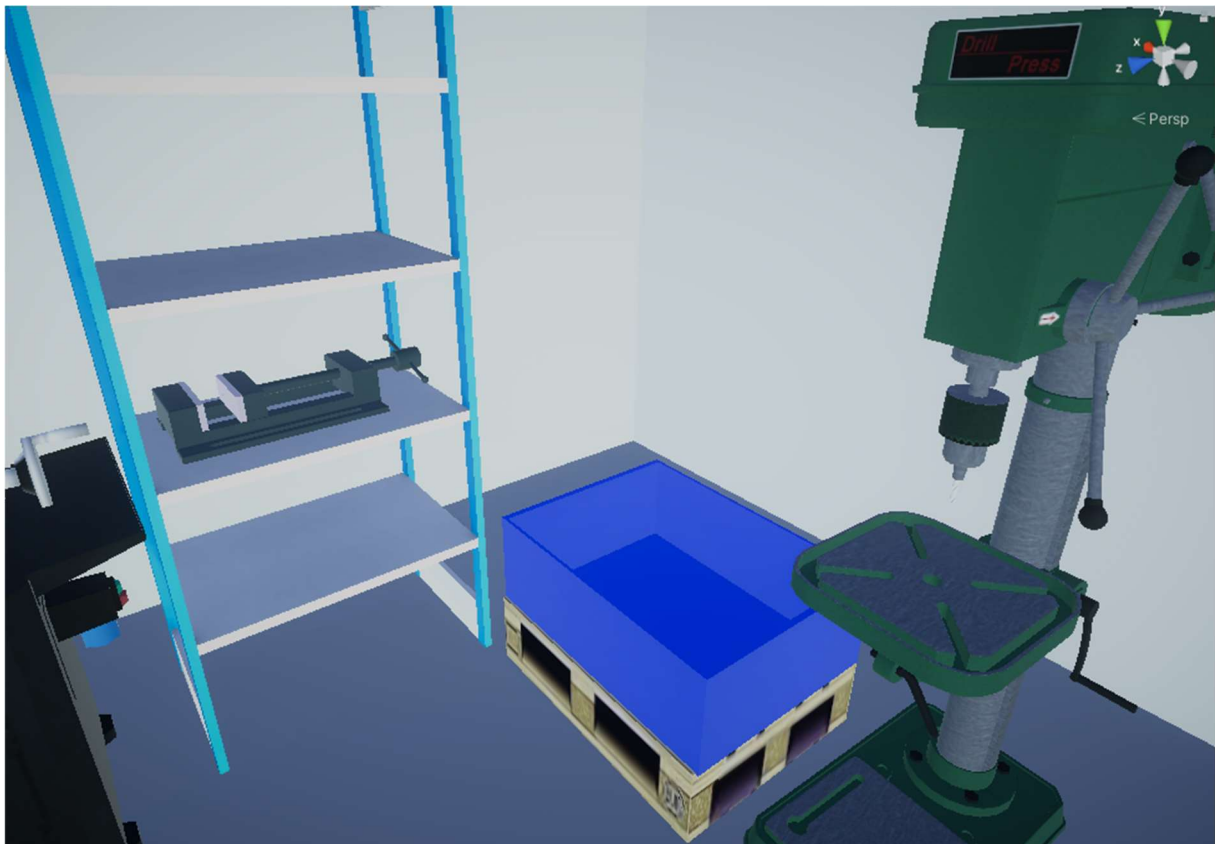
Snímek ze hry – vkládání polotovaru do soustruhu
